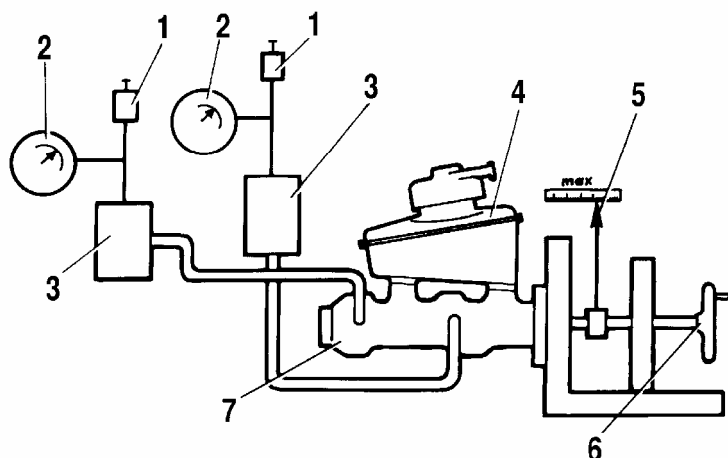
Схема проверки герметичности главного цилиндра:
